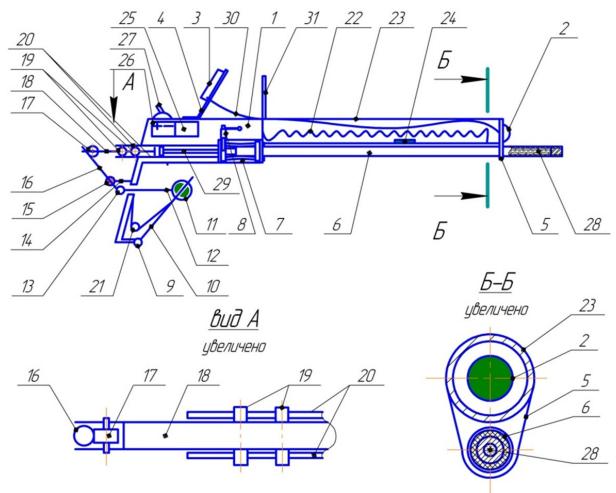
Схема аппарата для искусственного осеменения: 1 – корпус; 2 – мини-видеокамера; 3 - мобильный телефон; 4 – кронштейн; 5 – заглушка; 6 - шприц осеменатора; 7 - посадочное место под шприц; 8 – фиксатор; 9 – шарнир; 10 – кулиса; 11 - шарнир-ползун; 12 – шатун; 13 – шарнир; 14 – кронштейн; 15 – ось; 16 – рычаг; 17 – ролик; 18 – толкатель; 19 – бобышки; 20 – направляющая; 21 - возвратная пружина; 22 – нагреватель; 23 – трубка; 24 - датчик температуры; 25 – терморегулятор; 26 - батарея питания; 27 – выключатель; 28 – порция семени; 29 – поршень; 30 – кабель; 31 – упор
